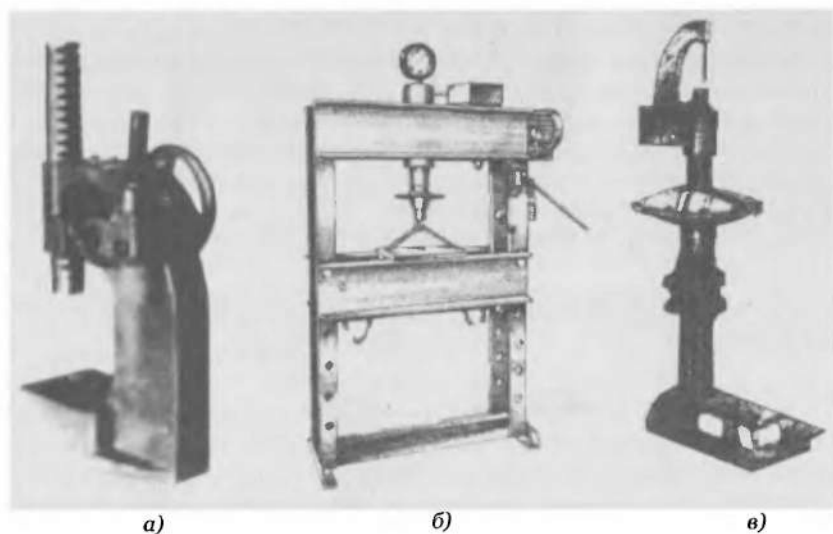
Различные прессы для разборочно-сборочных работ: *а* — электрогидравлический напольный пресс 2135-1М с дополнительным плунжерным насосом и ручным приводом для разборки и сборки мелких узлов; *б* — пневматический напольный пресс Р-304 для клепки фрикционных накладок; *в* — настольный пресс ОКС-918 с реечным приводом
